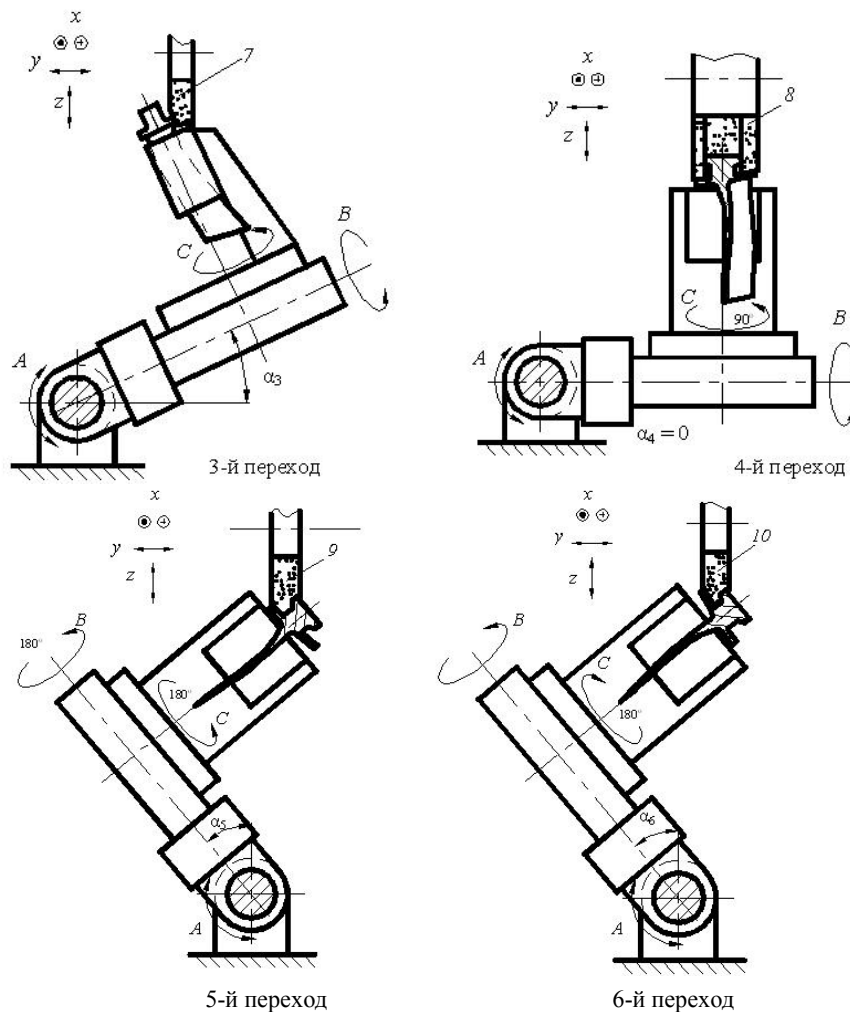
Схема взаимных перемещений инструментов и заготовки при шлифовании хвостовика рабочей лопатки 1 ступени компрессора двигателя SaM-146 (3 – 6 переходы)
